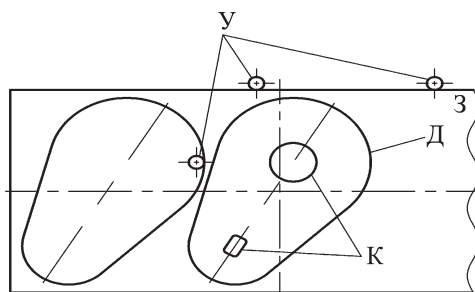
Внешний контур детали Д с пробиваемым внутренним контуром К, заготовка полоса материала З и упоры У в рабочей зоне штампа
